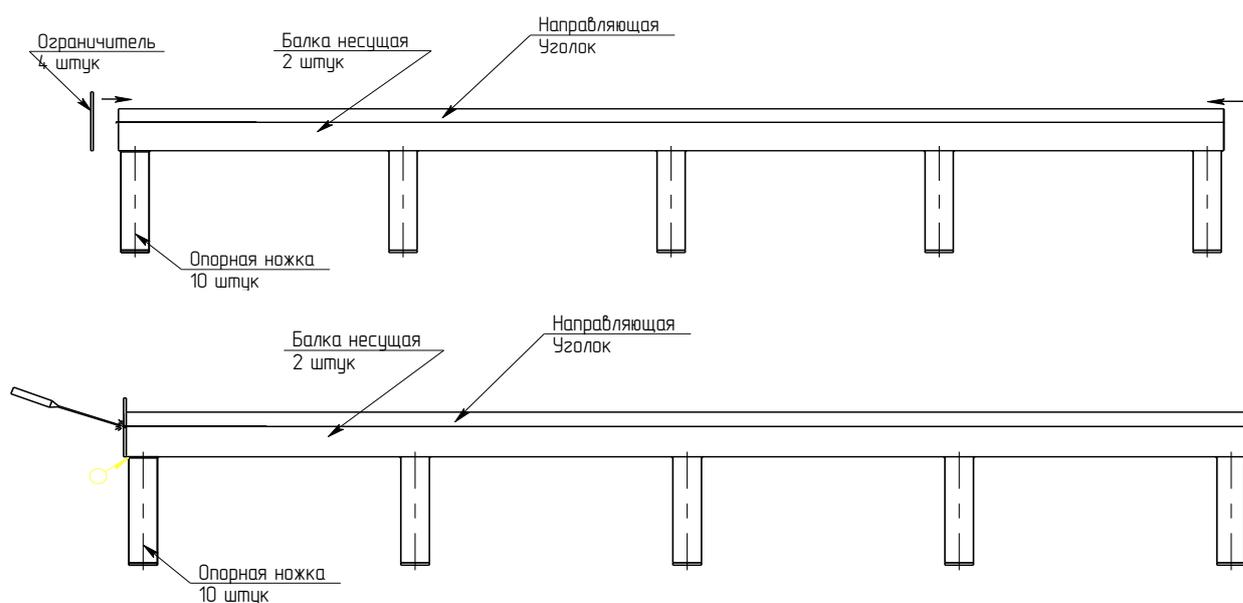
Установка ограничителя на края стола с помощью сварки
